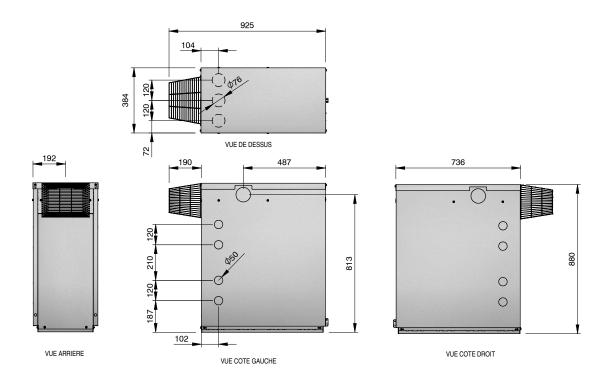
Dimensions Vortex Bas NOx Outdoor 18kW et 24kW
